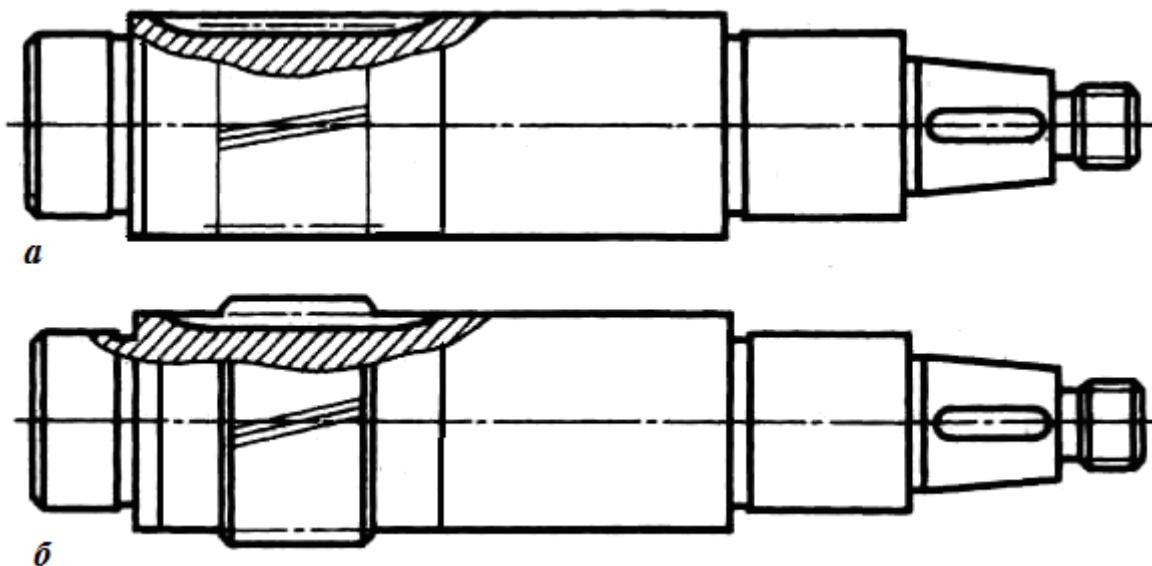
Валы-шестерни цилиндрической передачи *a* – зубья врезаны в вал, *б* - зубья нарезаны на поверхности вала
